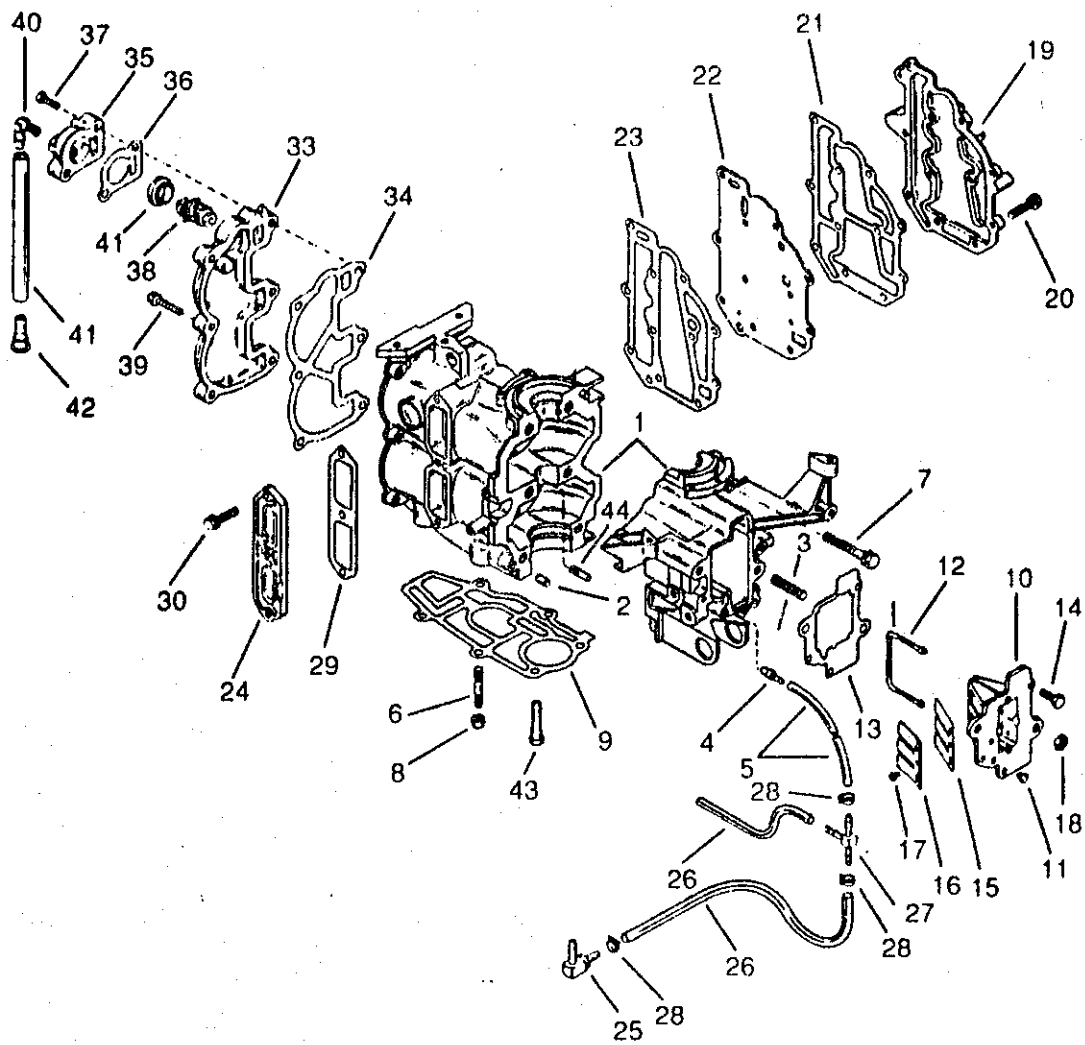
Bloque de cilindros, motor de 2 cilindros.
